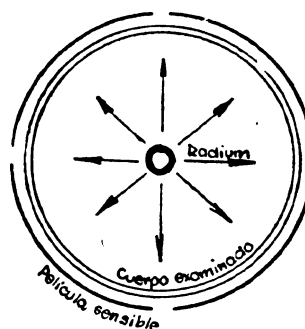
Método de examen de soldaduras circulares por medio del radium.
